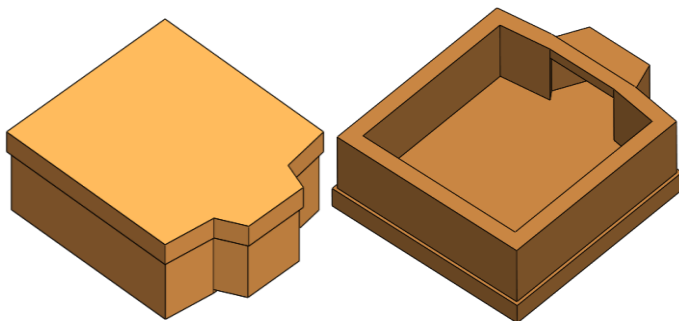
Modelado 3D del Refractorio en vista isométrica y planta
